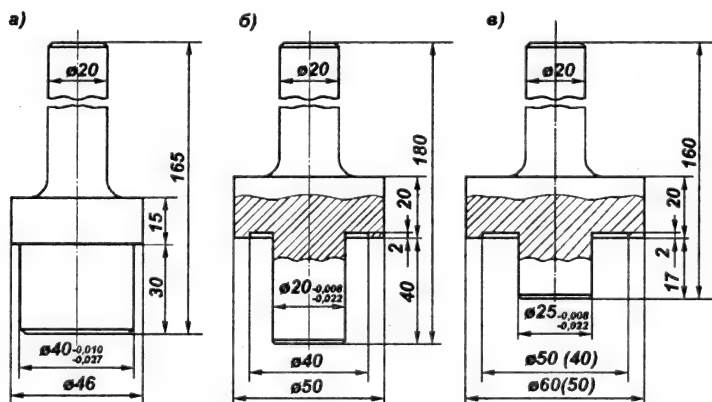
Оправки для запрессовки подшипников коренных опор коленвала
